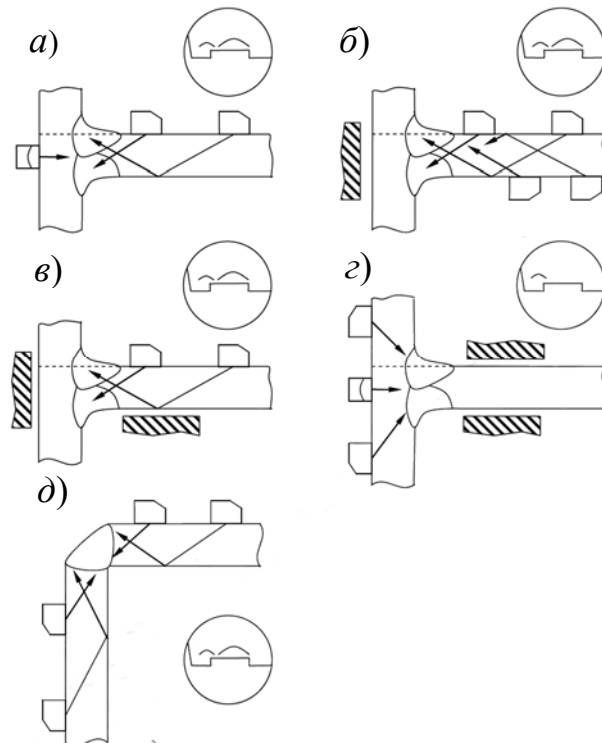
Схемы контроля тавровых и угловых сварных соединений
